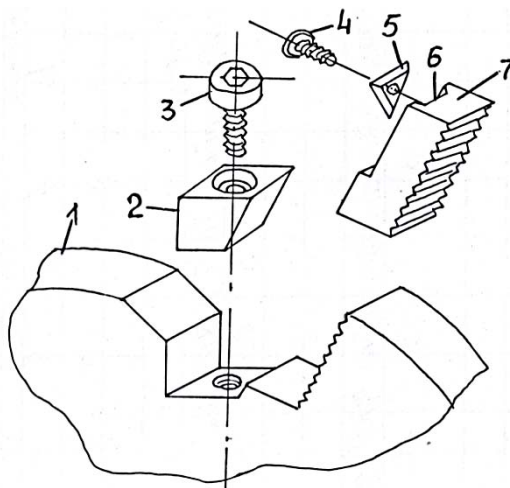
Узел крепления пластины трехсторонней дисковой фрезы Novex
